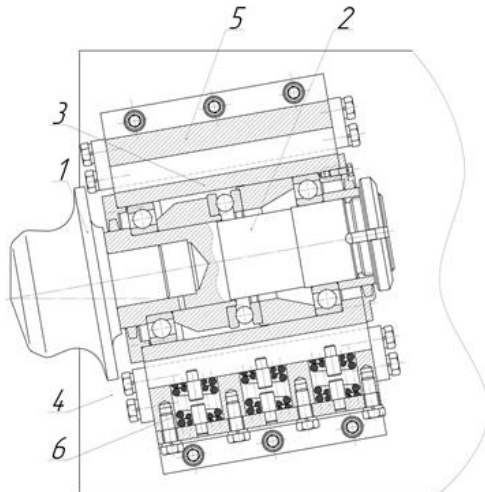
Блок обкочувального ролика до лоботокарного верстата ЛТ2
